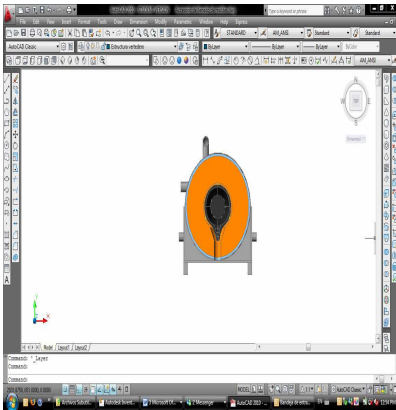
Imagen en planta mostrando la separación de cuñas de apoyo del crisol.
